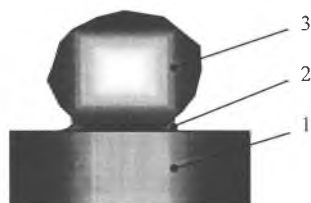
Схема закрепления зерна на поверхности связки: 1 – связка; 2 – галтель соединяемого металла; 3 – алмаз.
